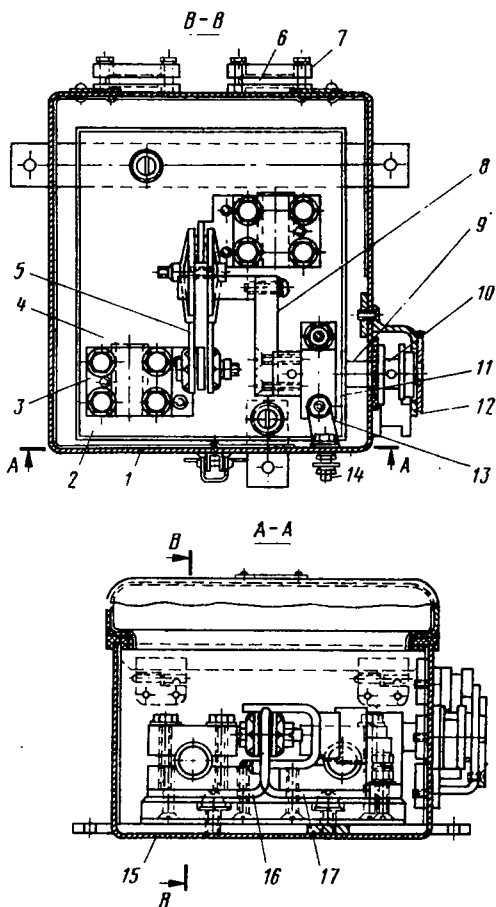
Общий вид разъединителя ГВ-10Ж
